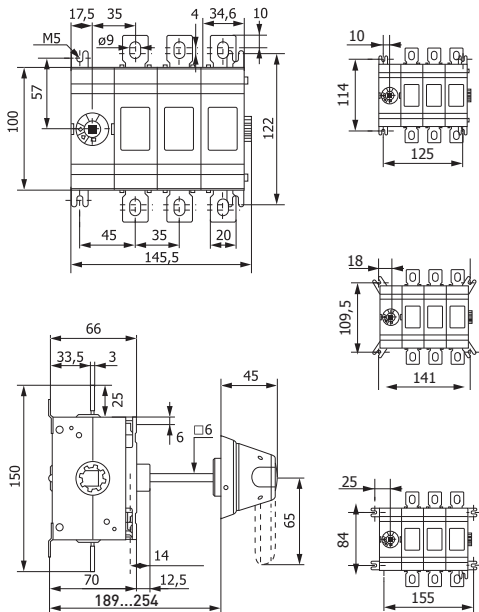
Габаритные и установочные размеры рубильников 160-250 А 3Р
